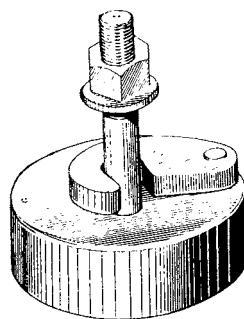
Приспособление 47001-1-014П для сжатия пружин блокировочного фрикциона планетарного механизма поворота
